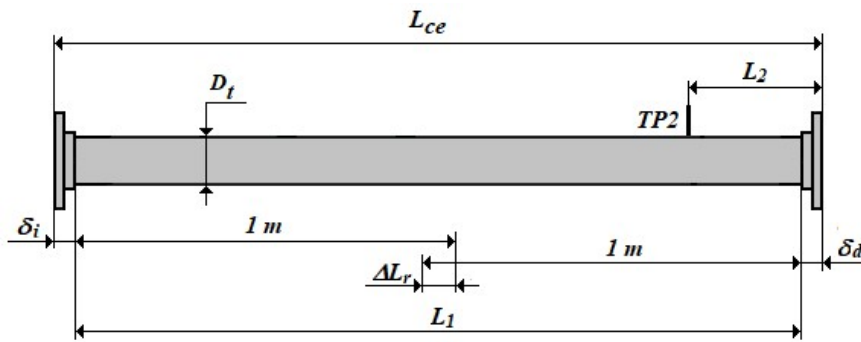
Prototipo TC-01-(0.4/2). Dimensiones de la cámara de expansión.
